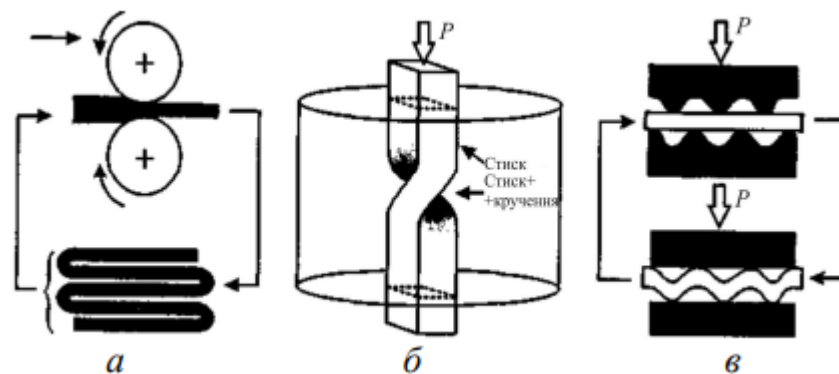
Схеми СПД: а багатократна прокатка; б екструзія крізь фільтру з гвинтовим перерізом; в багатократне гофрування розправлення Для зміцнюючої обробки поверхні розроблено багато схем, що забезпечують формування нанокристалічної структури приповерхневих шарів (рис. 1.13).
